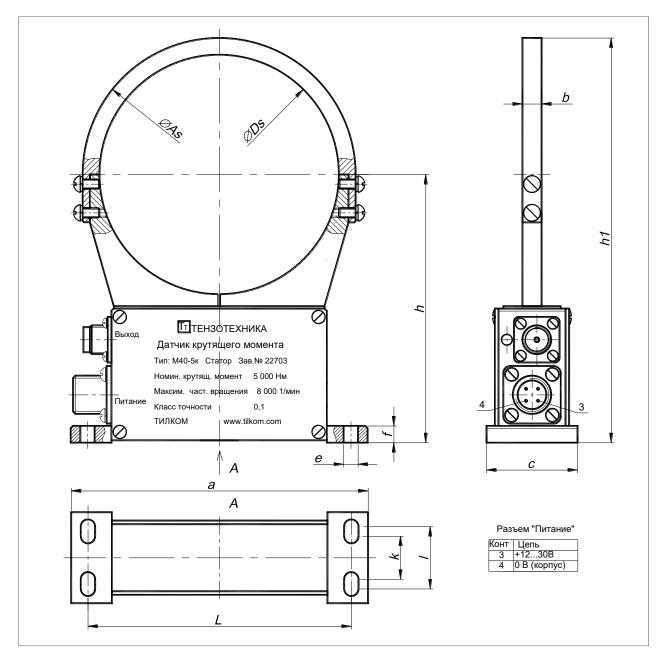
Статор М40-400... М40-6к. Габаритные и установочные размеры, мм
